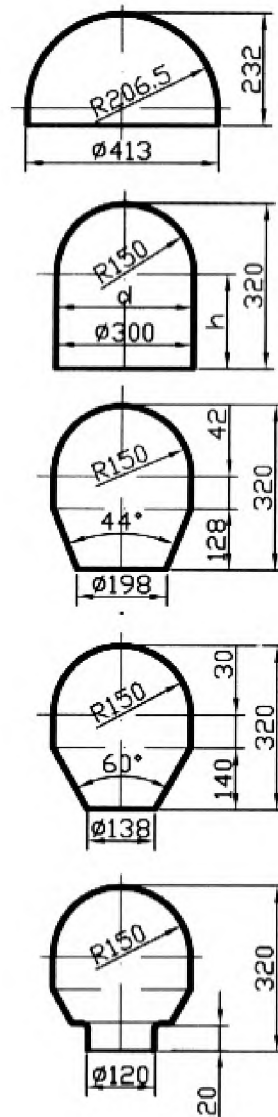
Формоизменение заготовки при изготовлении цельноштампованной оболочки
